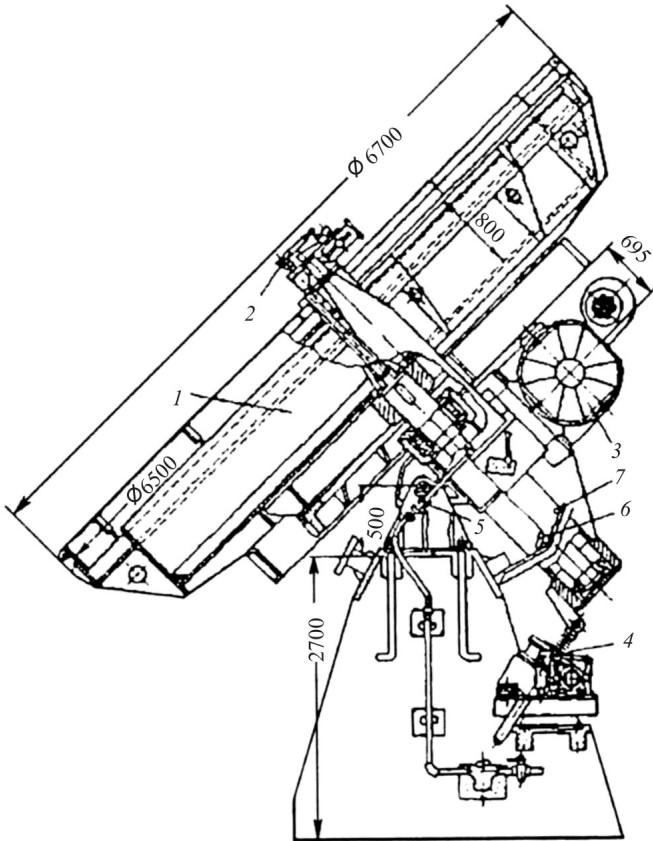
Чашевый окомкователь: 1 – чаша; 2 – установка скребков; 3 – привод чаши; 4 – механизм регулирования угла наклона; 5 – опора; 6 – копир; 7 – конечный выключатель
